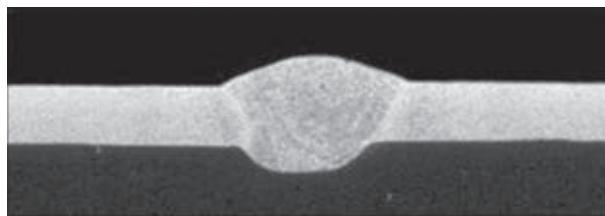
Макрошлиф сварного соединения из сплава Д16 толщиной 2 мм, сваренного плазменно-дуговой сваркой в нижнем положении
